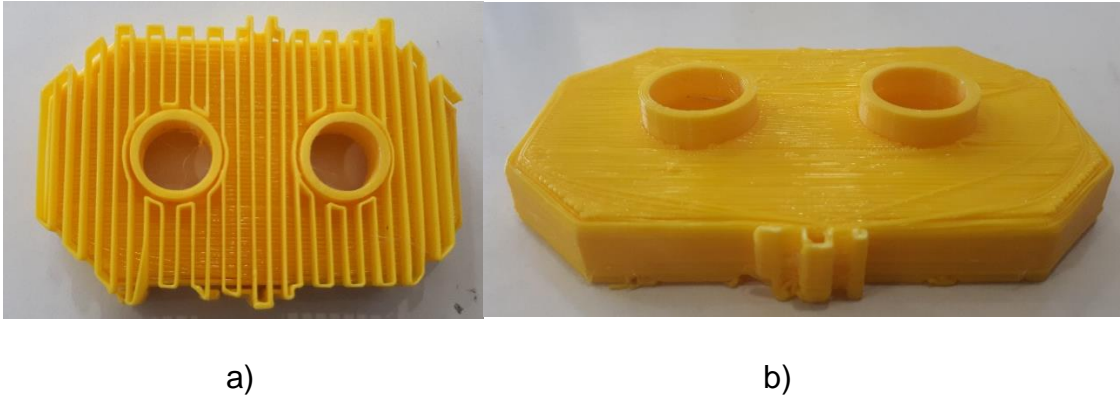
Pieza fabricada con PLA color amarillo por extrusión de material con desprendimiento mecánico. a) Pieza con soporte. b) Pieza sin soporte.
